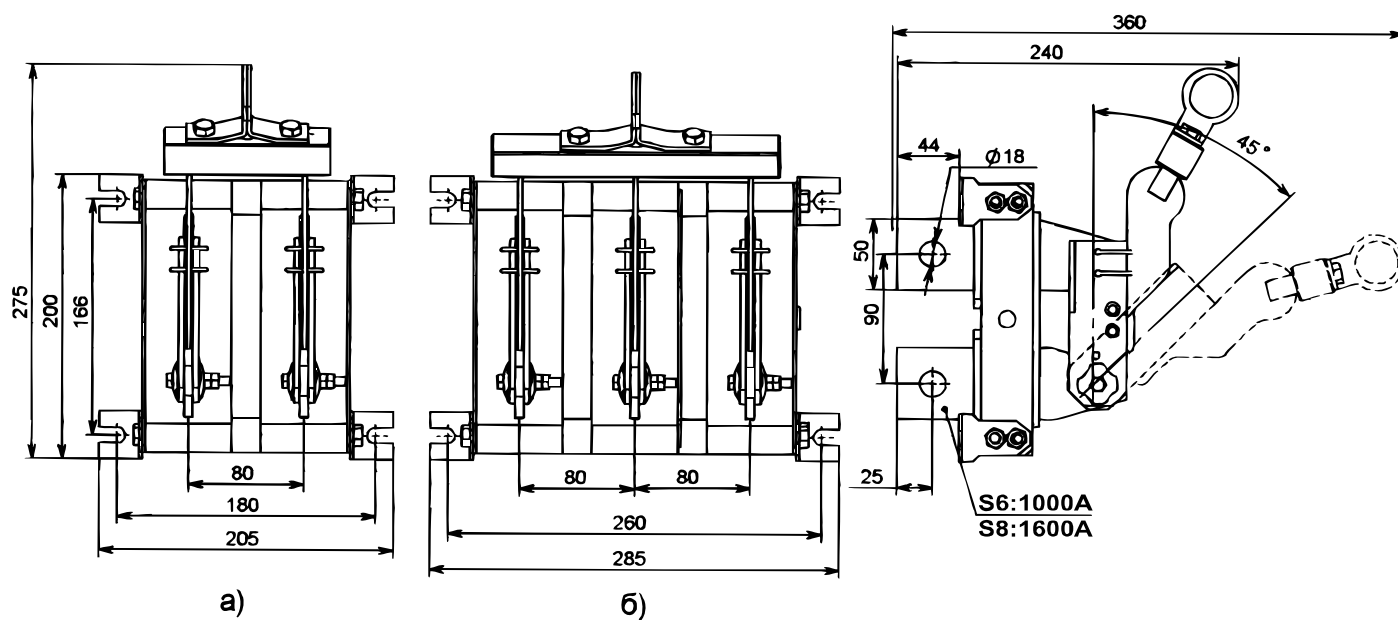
Разъединитель РЕ19 с центральным рычагом для управления штангой, заднего присоединения шин
